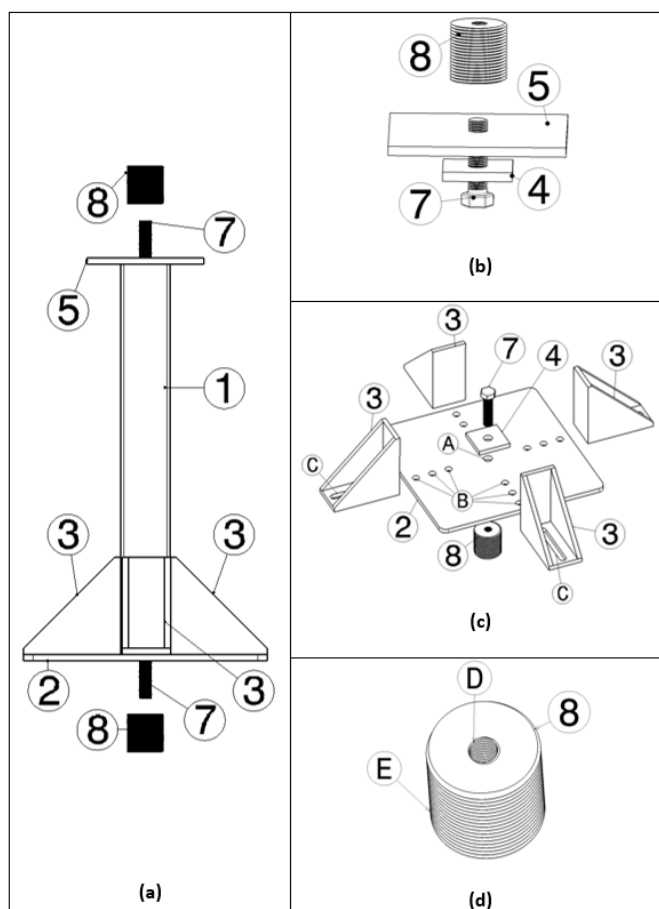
Detalhes da adequação da máquina de ensaios: (a) montagem do conjunto, (b) parte superior, (c) parte inferior e (d) adaptador com rosca
